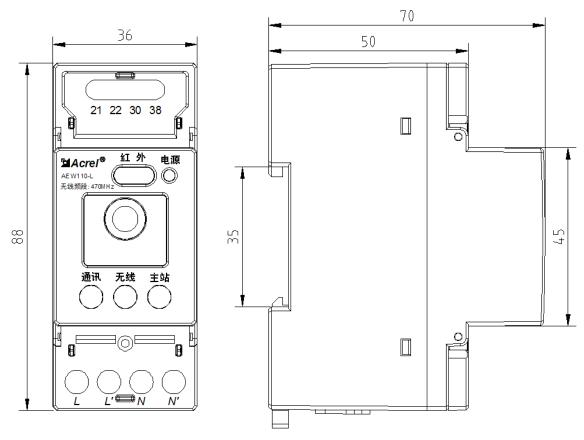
无线通讯转换器外形尺寸 Fig. 1 Overall dimensions of wireless communication converter
